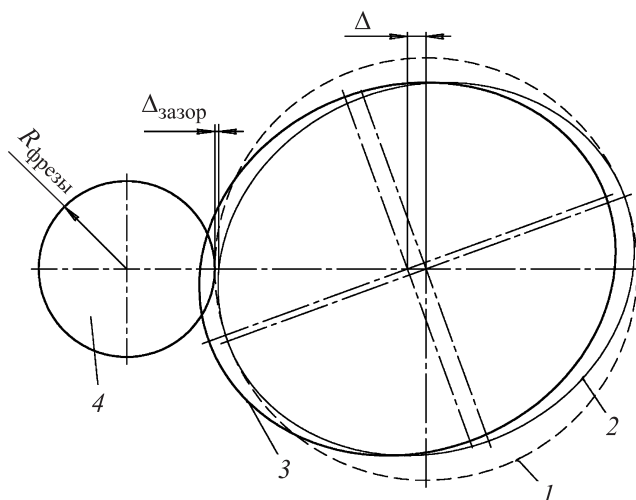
Обработка шлифовальным кругом заготовки фрезы:
